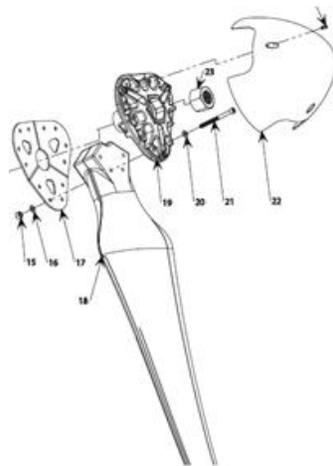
Conjunto de cuchilla y ojiva [8].
